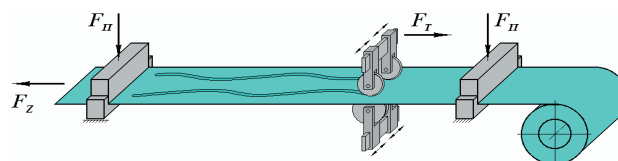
Способ изготовления профилей с продольными криволинейными гофрами
